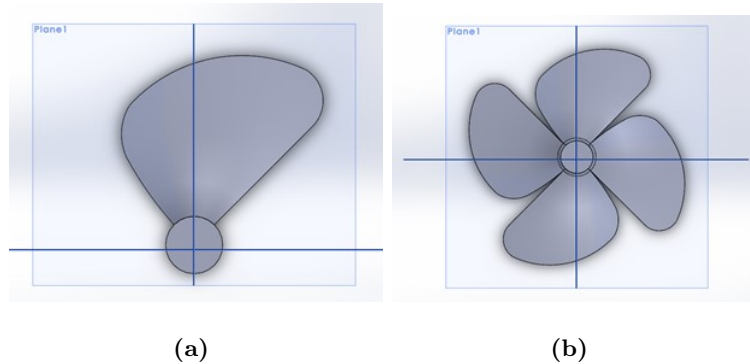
En esta imagen se presentan dos vistas de la propela. a) Vista final del diseño de un aspa, b) vista superior de las aspas.
